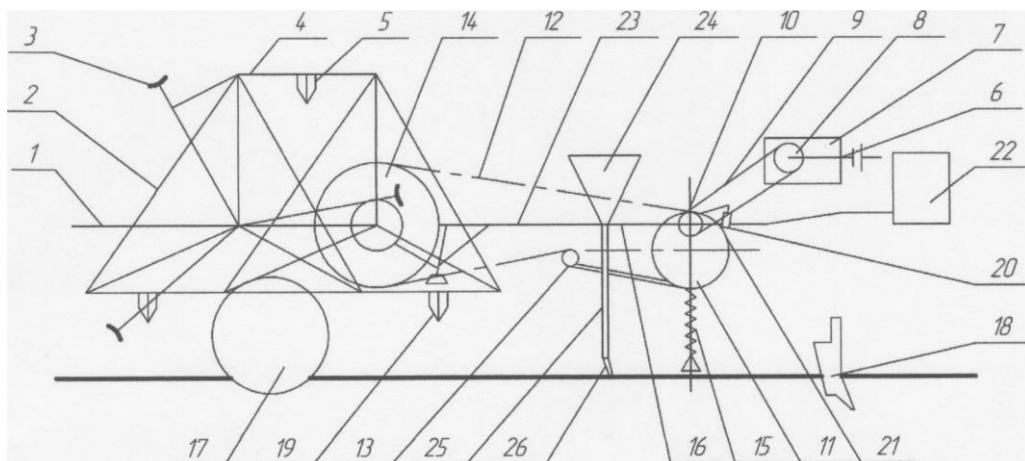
Схема установки для посадки корнеплодов (вид сбоку)
